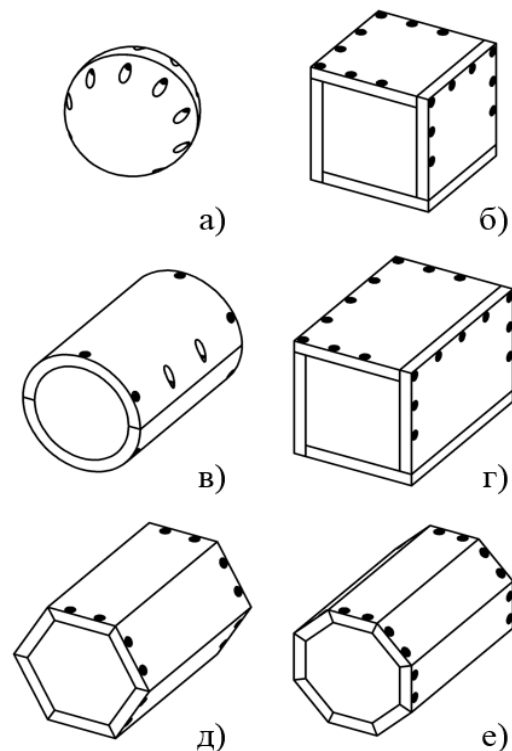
Можливі форми корпусу реєстратора: а) – кулеподібний; б) – кубічний; в) – циліндричний; г) – паралелепіпед; д) – шестикутна призма; е) – восьмикутна призма
